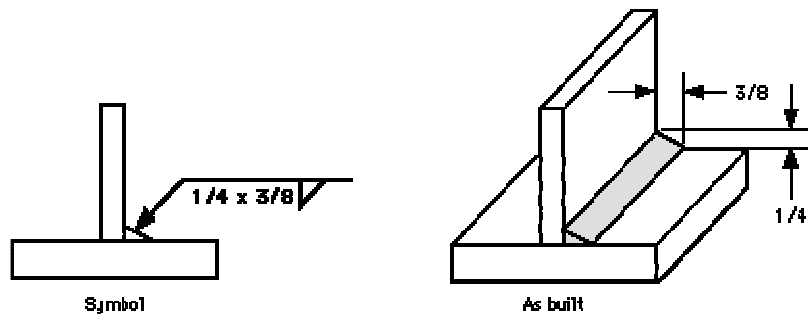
Aplicación de símbolos de soldadura de filete
